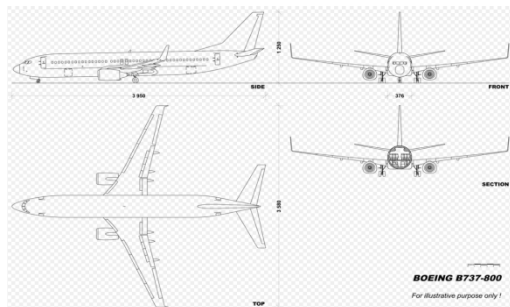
Plano de detalle e imagen del Boeing 737-800 (Fuente: Wikipedia)
